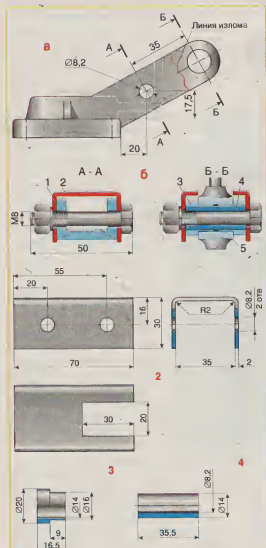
Ремонт шарнира рычага блокировки дифференциала: а — разметка отверстий в кронштейне; б — шарнир в сборе (1 — кронштейн; 2 — скоба; 3, 4 — втулки; 5 — рычаг).
